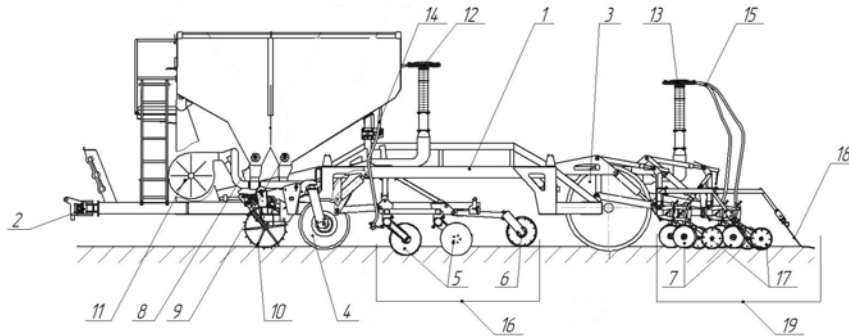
Конструктивная схема почвообрабатывающе-посевного агрегата АПП – 9
